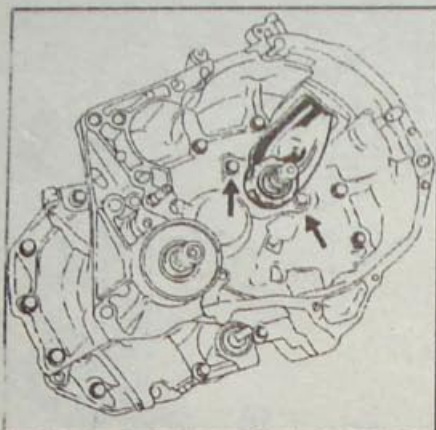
Расположение болтов крепления направляющей втулки подшипника выключения сцепления
